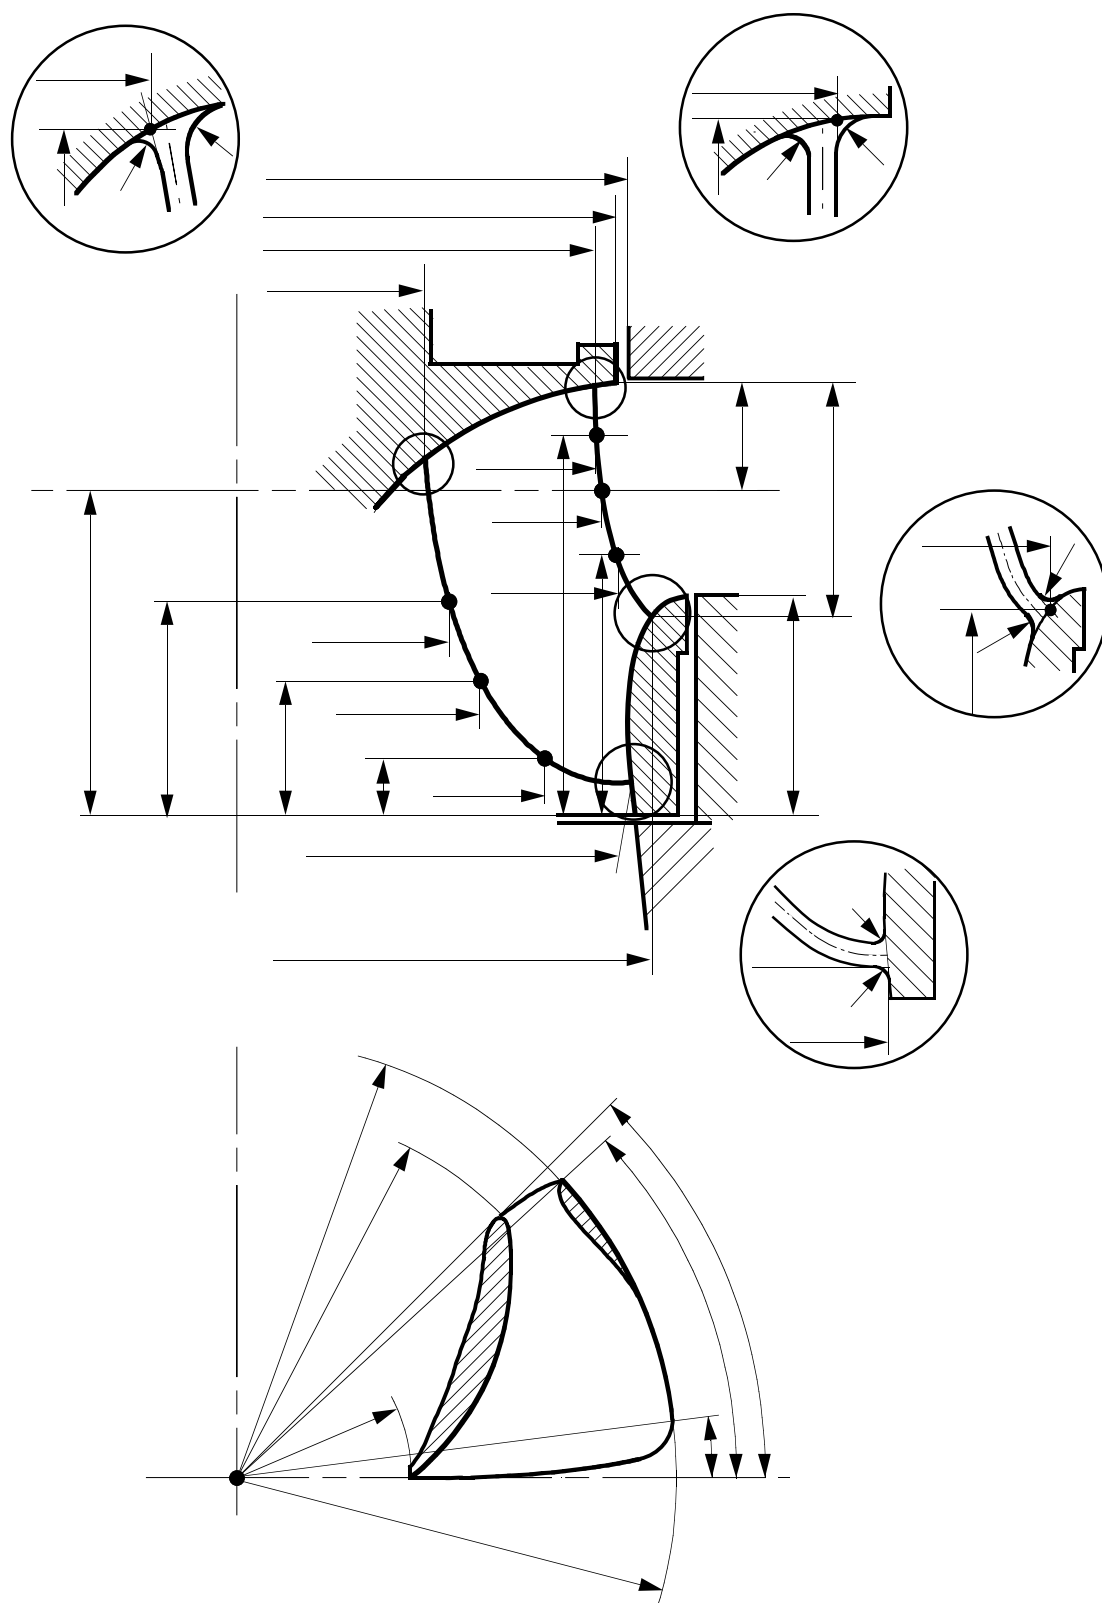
Exemple des dimensions à contrôler sur la roue d'une machine radiale
